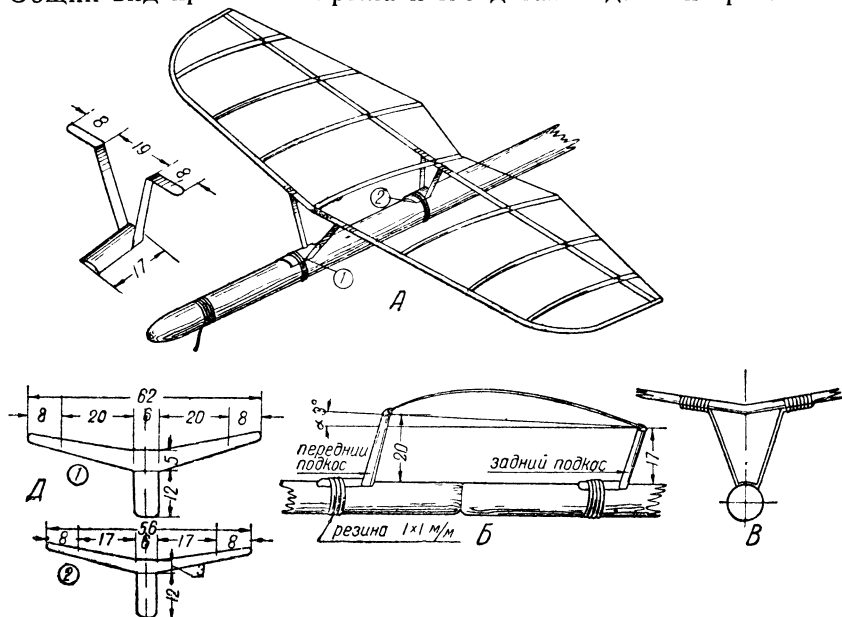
Крепление стабилизатора: А — общий вид крепления; Б — вид крепления сбоку; В — вид крепления спереди; Г — общий вид подкоса; Д — рабочие развертки подкосов
